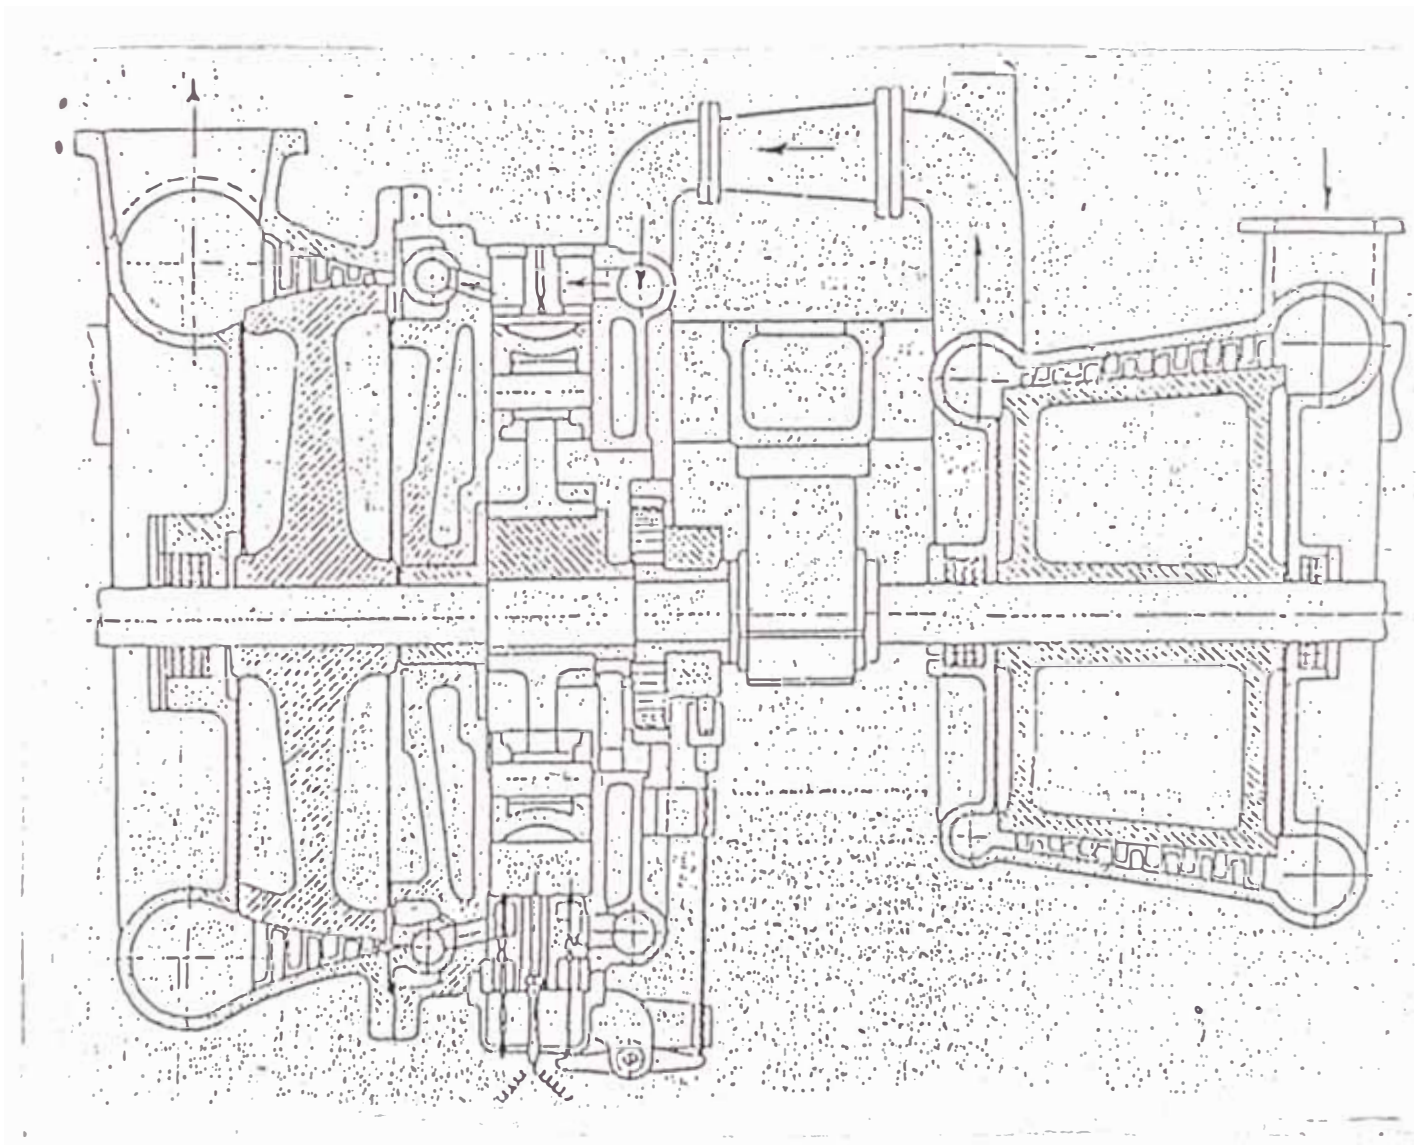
Motor sobrealimentado diseñado y construido por Buchi.
